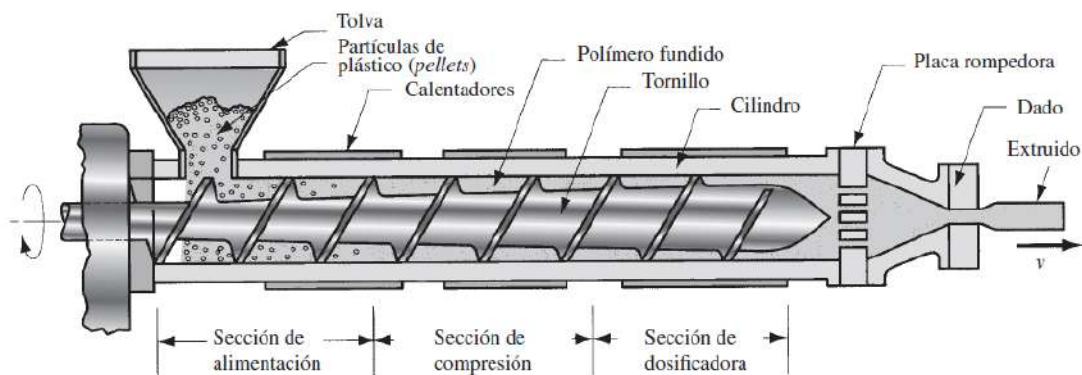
Componentes de una máquina extrusora de un solo tornillo para plásticos y elastómeros [1]
